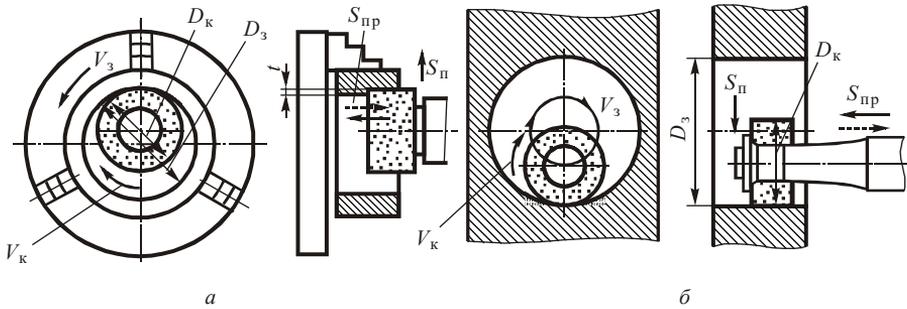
Схемы внутреннего шлифования отверстия во вращающейся детали (а) и в неподвижной детали — планетарное шлифование (б)
